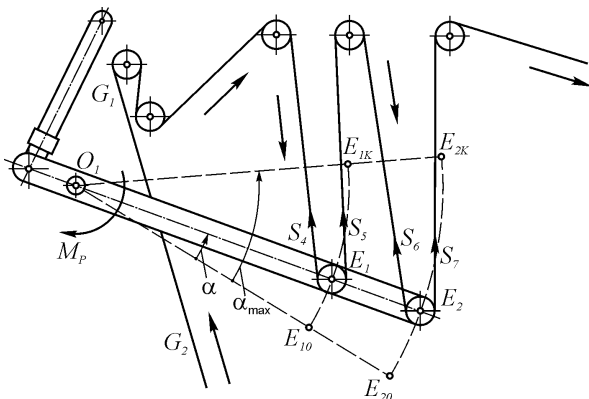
Схема частини пасової передачі, що охоплює валики важеля натяжного пристрою
